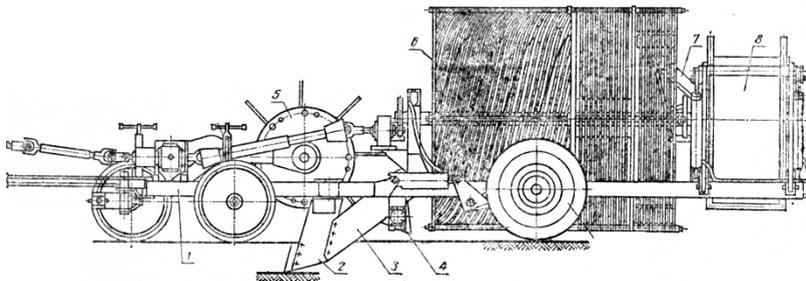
Схема камнеуборочной машины KBM-1,4: 1 – рама; 2 – лемех плоский; 3 – решетка прутковая; 4 – вал измельчительный; 5 – ротор; 6 – барабан сепарирующий; 7 – устройство направляющее; 8 – бункер накопительный
